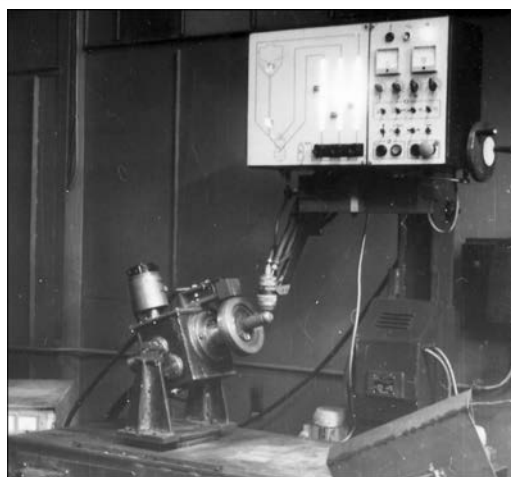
Установка для наплавки уплотнительных поверхностей штоков вентилей
